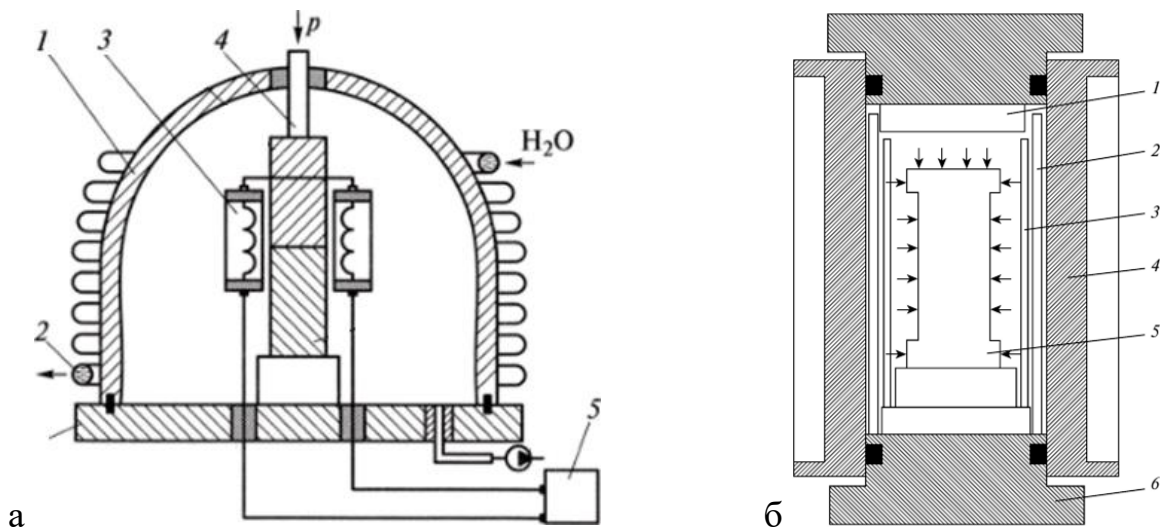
Схема сварного процесса в условиях традиционной диффузионной сварки (а) и горячего изостатического прессования (б)
